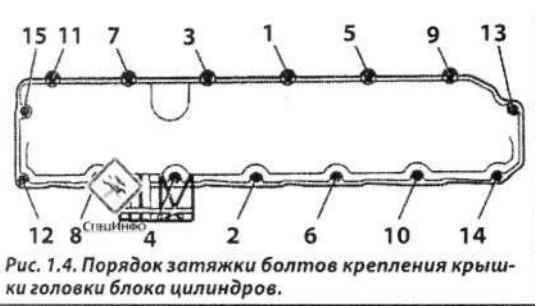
Порядок затяжки болтов крепления крышки головки блока цилиндров.
